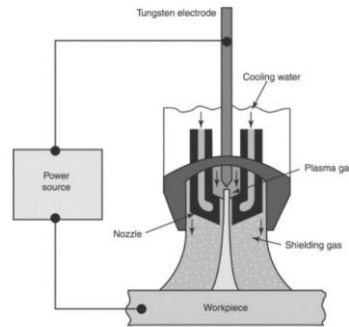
Esquema do processo de soldadura PAW [9].
